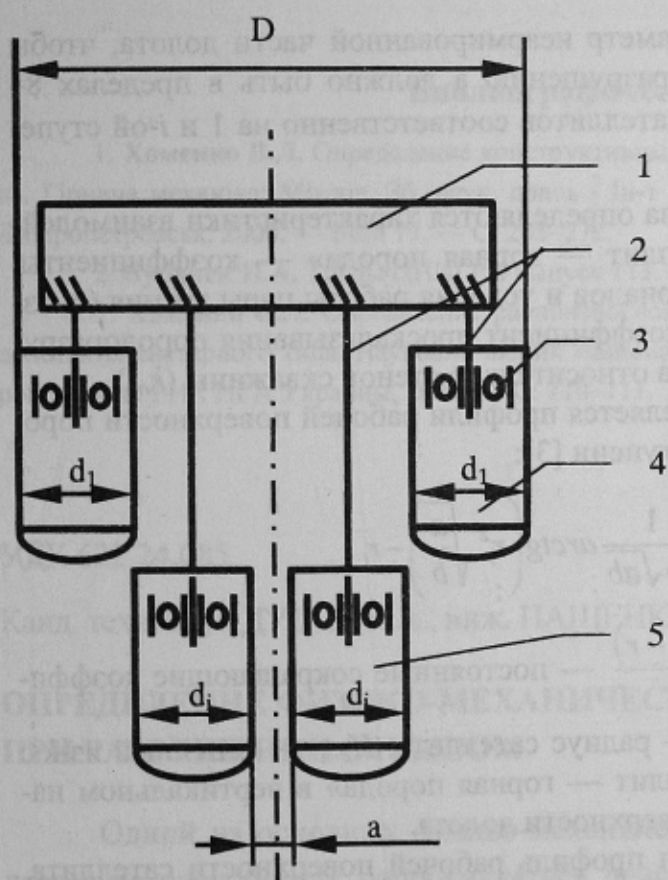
Принципиальная схема для определения конструктивных параметров планетарных долот: 1 — корпус долота; 2 — валы; 3 — подшипники; 4 — сателлиты первого ряда; 5 — сателлиты i -го ряда
